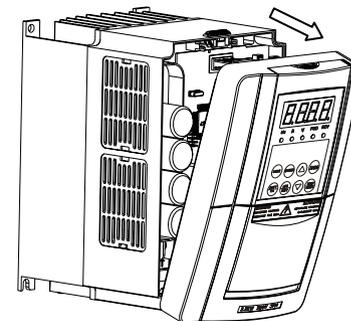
Демонтаж верхней крышки инвертора типа А
